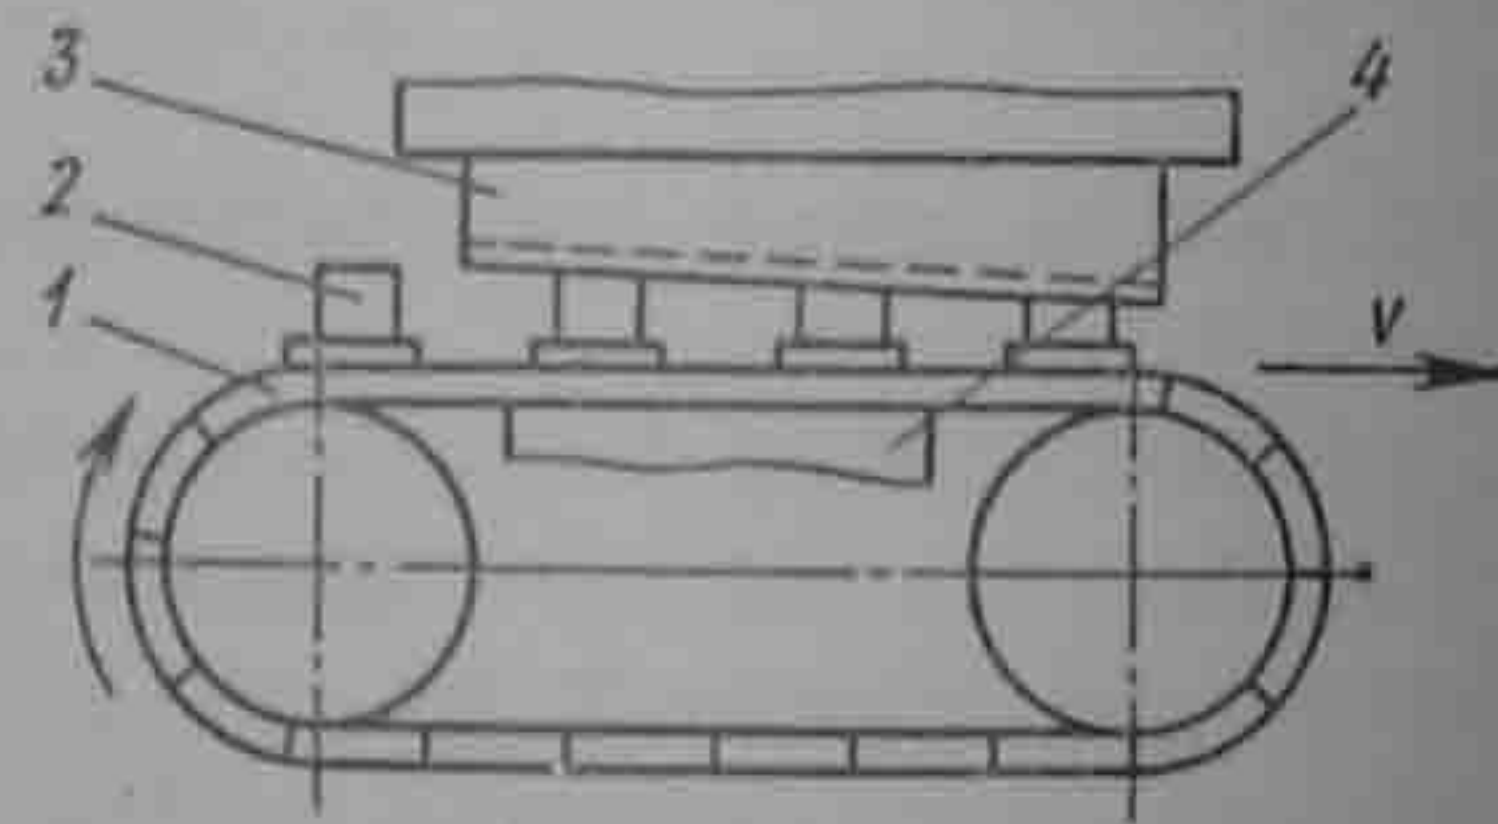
Схема обработки заготовок на протяжном станке непрерывной обработки
